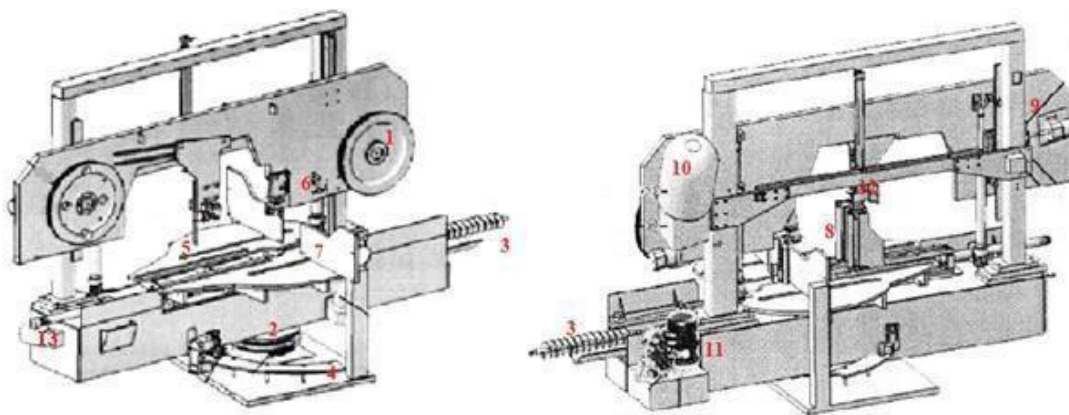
Estrutura pormenorizado do serrote semiautomático.
